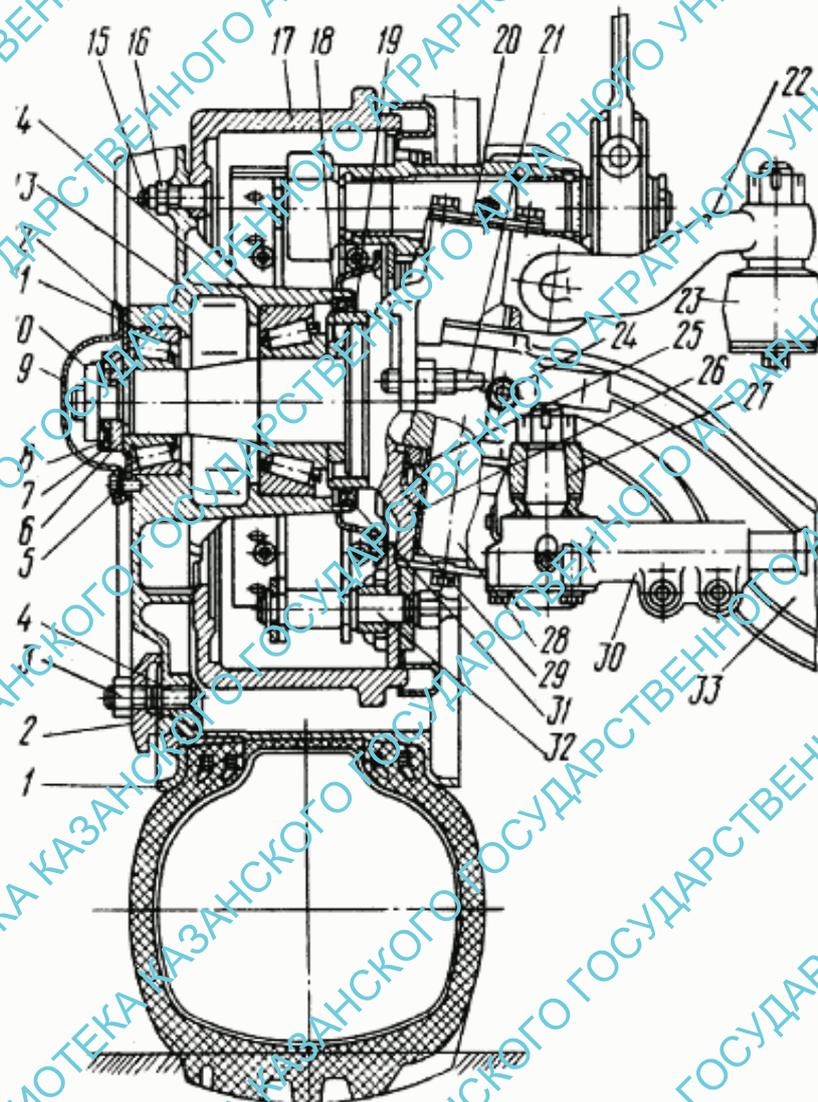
Передняя ось: 1 - колесо с шиной в сборе; 2 - прижим колеса; 3, 16 - гайки; 4 - шпилька; 5, 15 - болты; 6 - гайка подшипников; 7, 8 - шайбы, гайки и контргайки замковые; 9 - крышка ступицы; 10 - контргайка; 11, 14 - подшипники; 12 - прокладка; 13 - ступица; 17 - барабан тормозной; 18 - кольцо упорное; 19 - кольцо
